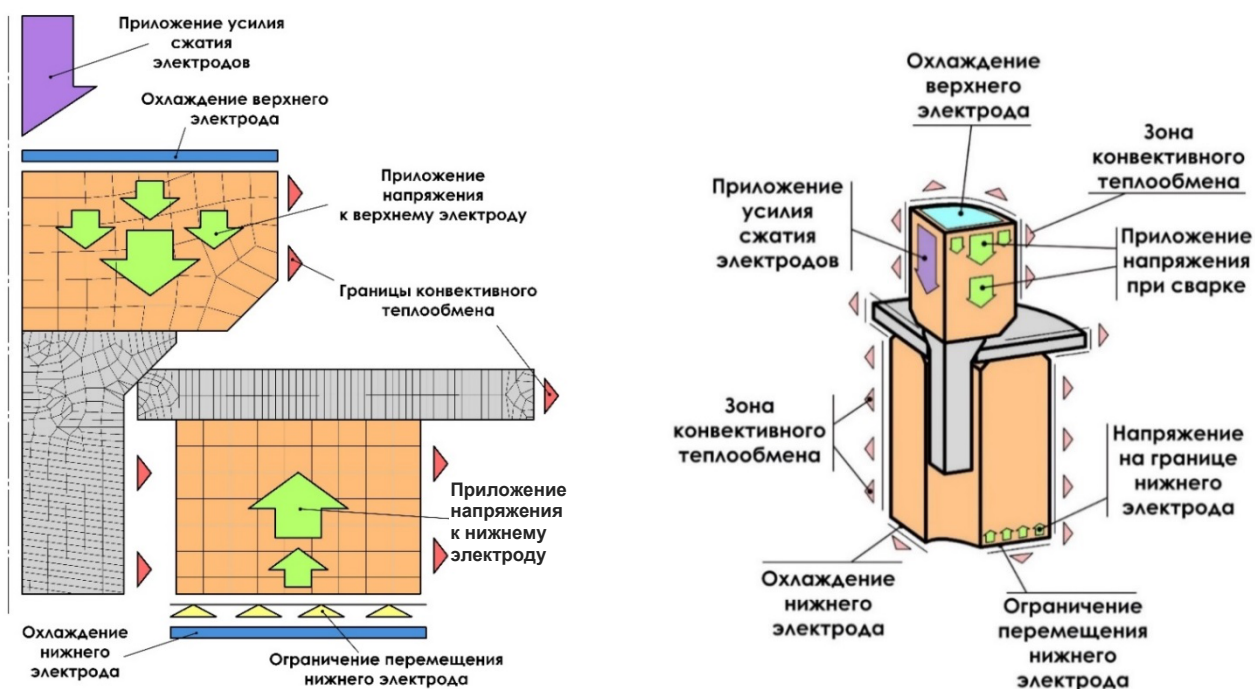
Расчетная схема математической модели исследуемого процесса контактной рельефной сварки Т-образных соединений
